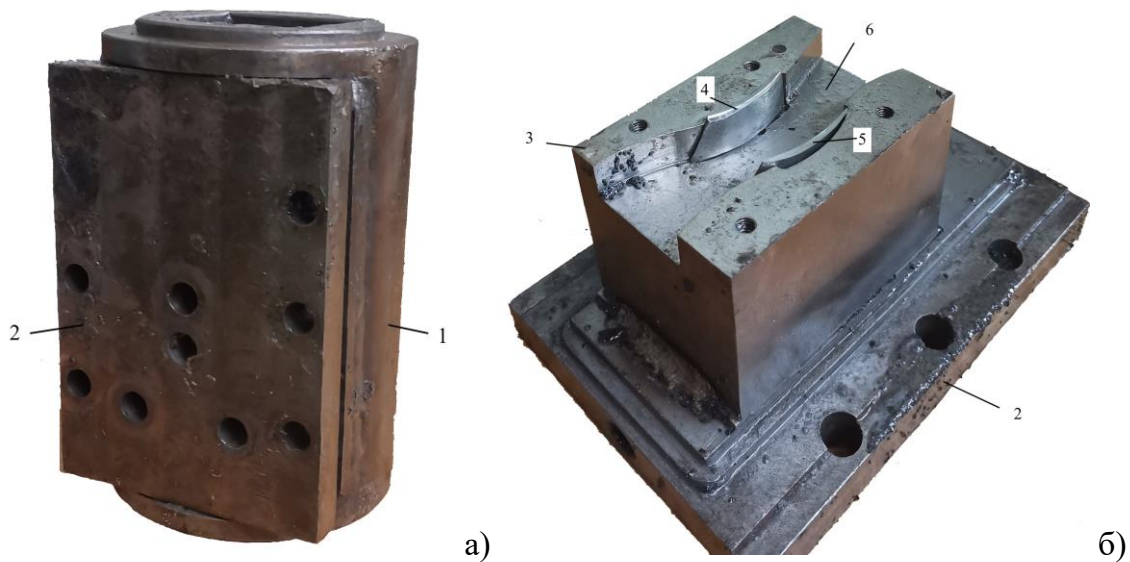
Приспособление – имитатор внутреннего канала литой заготовки: а) общий вид; б) съемная часть [2]
